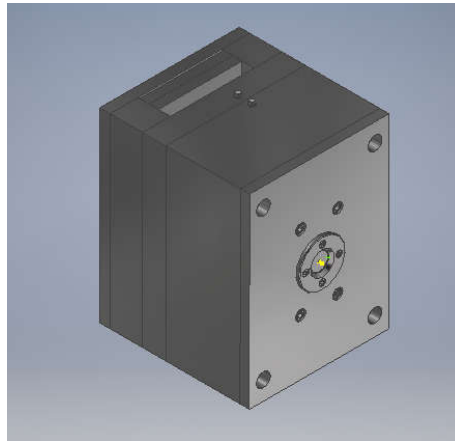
Molde estándar diseñado para la obtención de focos delanteros
